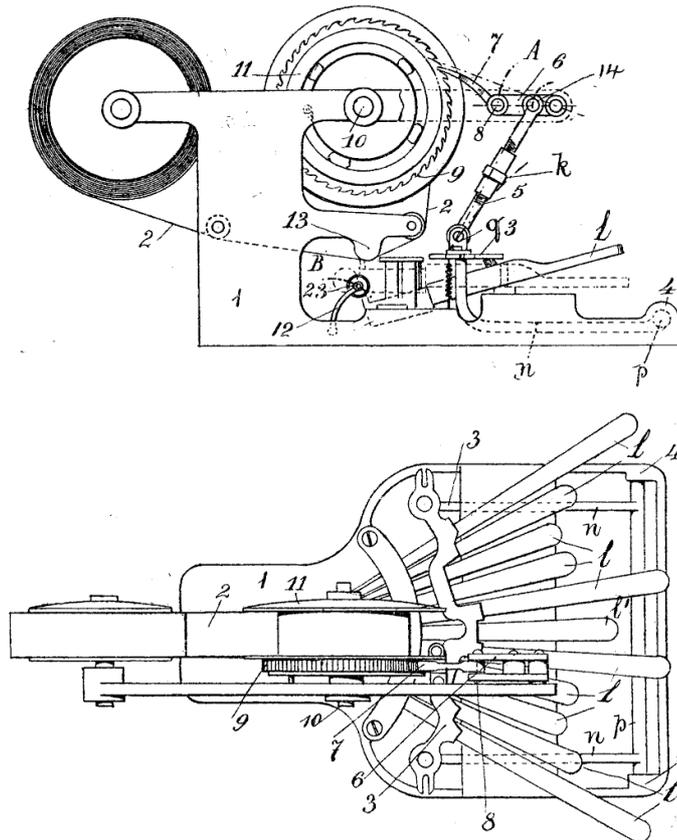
et 2. — Sténodactyle Lafaurie. Élévation et plan.
